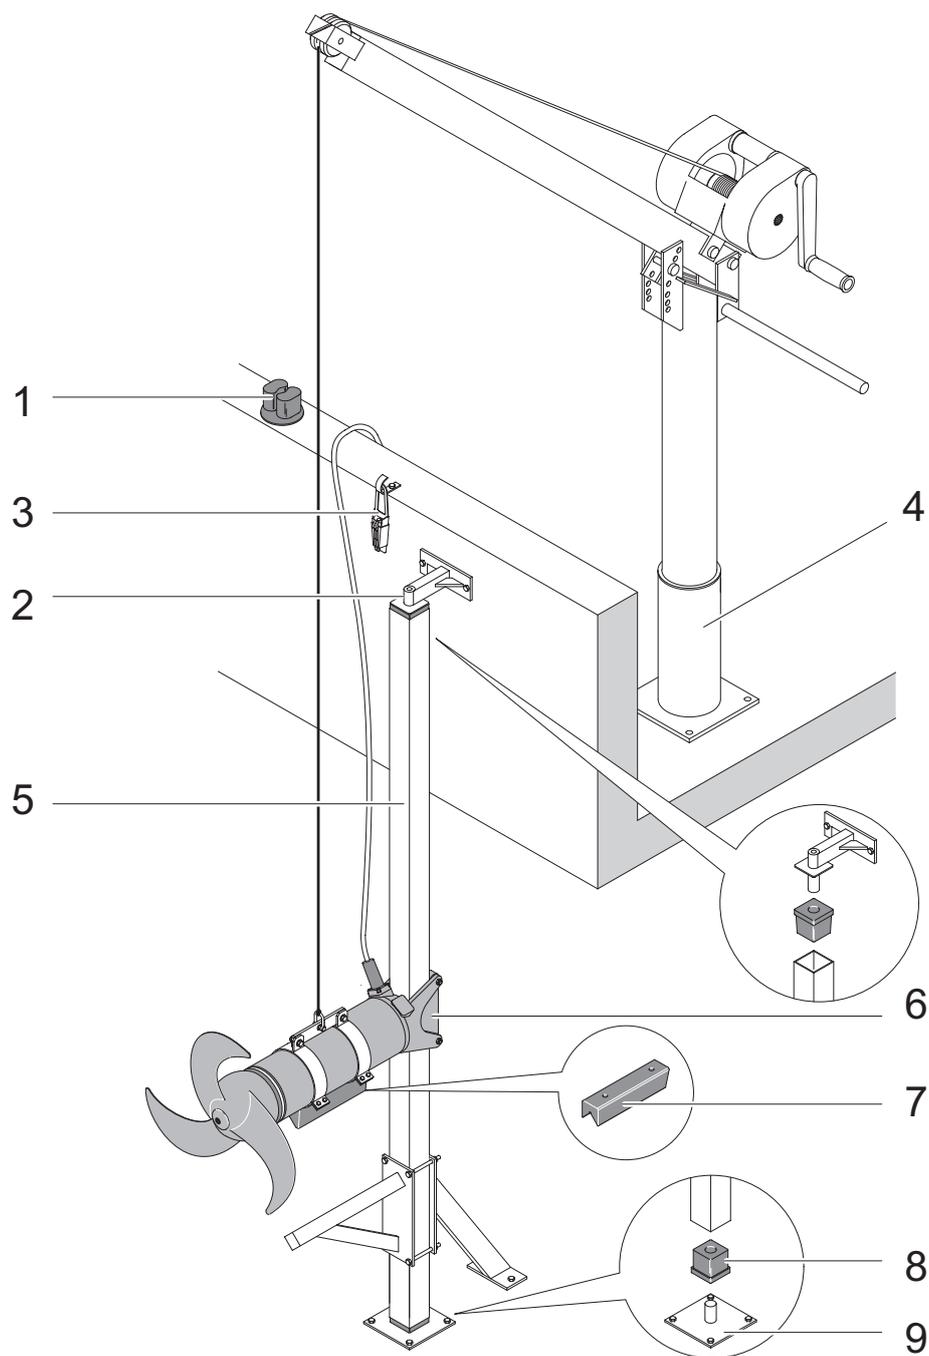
Esempio d'installazione con installazione fissa come acceleratore di flusso
